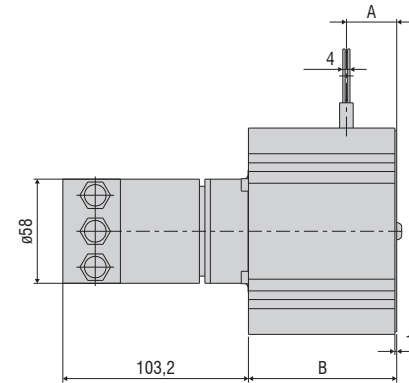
Maßzeichnung WDS- ... - P115 - BH - CO/PB/PN/ENIP/CAT
